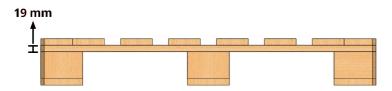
Esquema de vista lateral de um pallet com tábuas de ligação com 19 mm de espessura.
